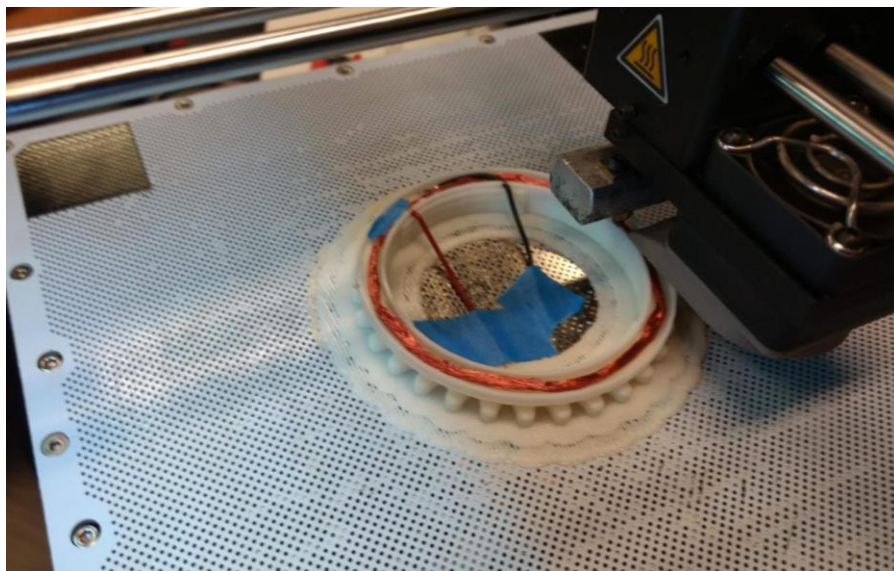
Montado de la bobina sobre cavidad del cuerpo del robot.
